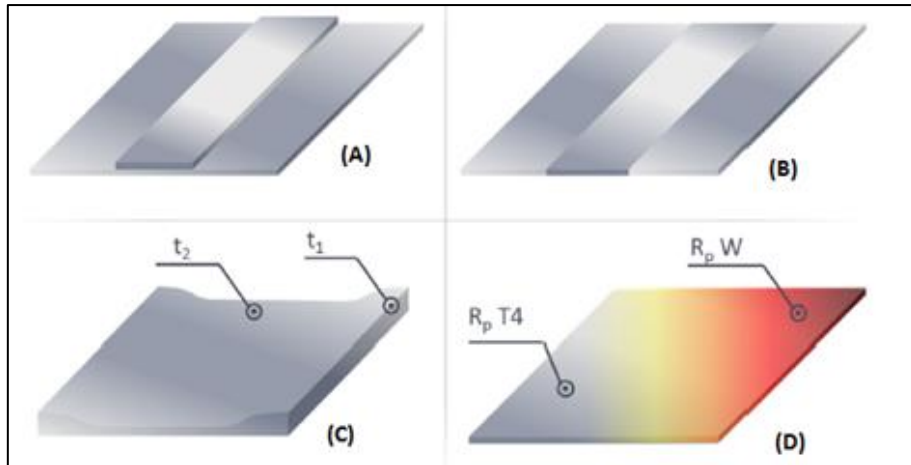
Diferentes processos de fabricação de Tailor Blanks. (A) Patchwork Blanks; (B) Tailor Welded Blanks; (C) Tailor Rolled Blank e (D) Tailor Heat Treated Blanks.
